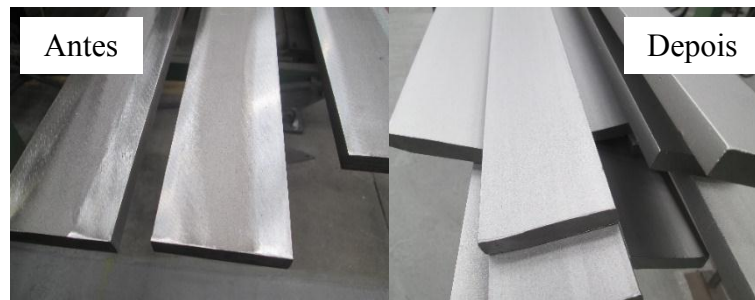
Barras antes e depois da passagem pela máquina de jatear
